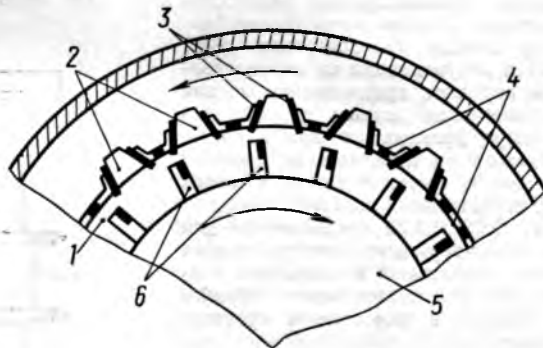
Зубчато-ситовая мельница на базе центробежного стружечного станка ДС-7:
